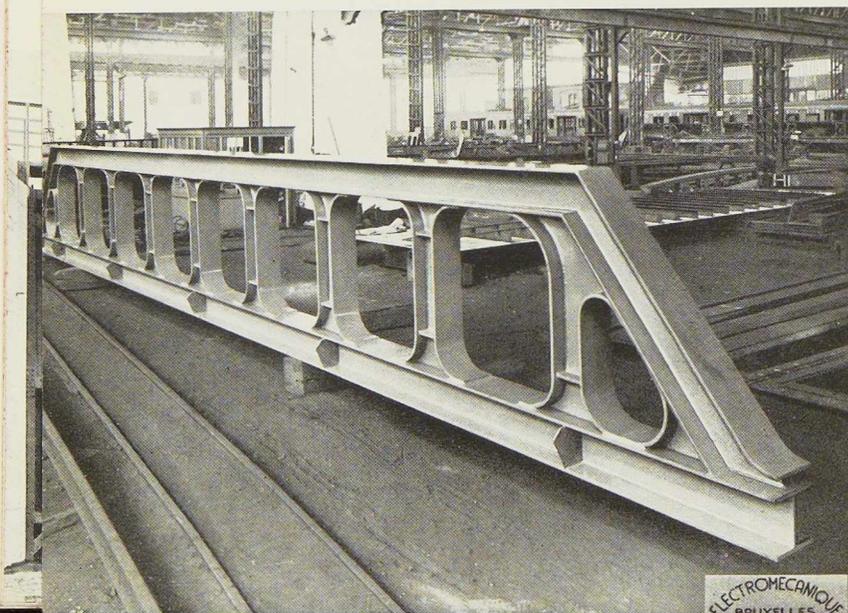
Vue de la poutre Vierendeel soudée de la vanne Stoncy.
